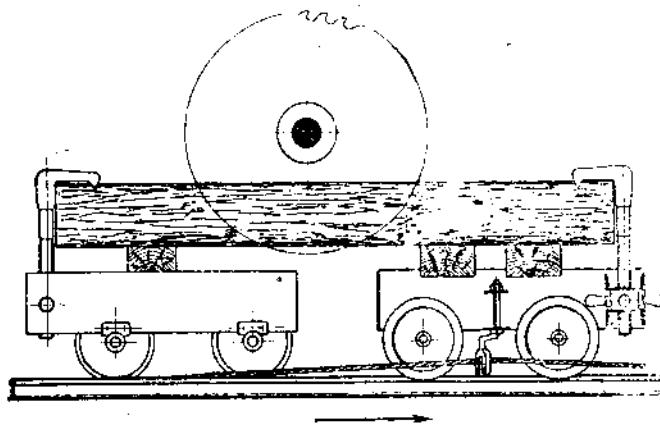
Круглопильный станок с механической подачей для окантовки бревен
